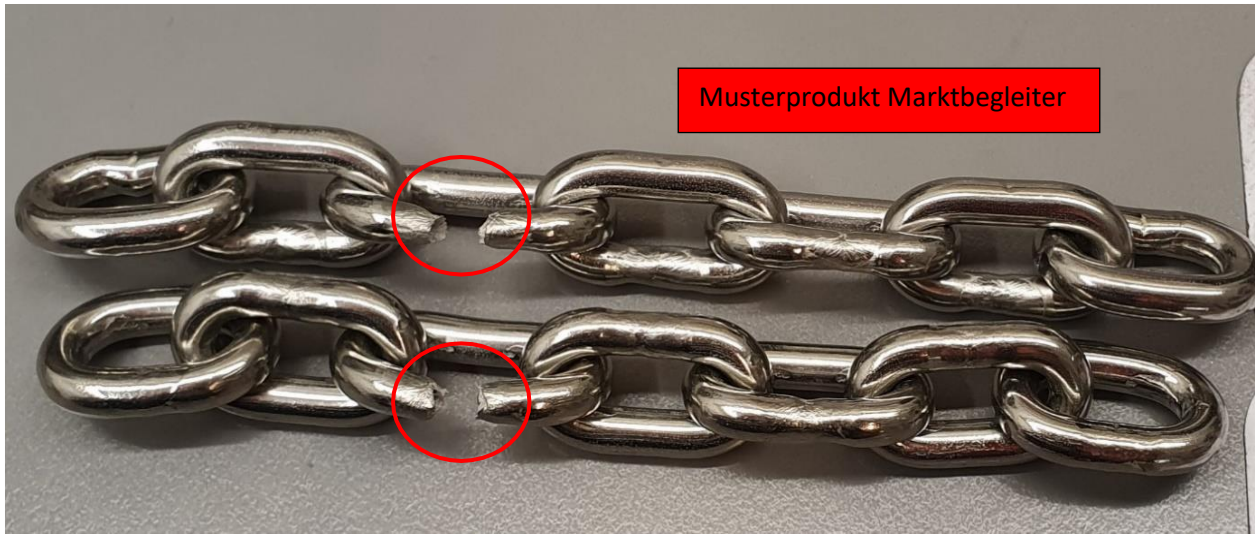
6x18,5 mm Schweißnahtbrüche beim Zugversuch
